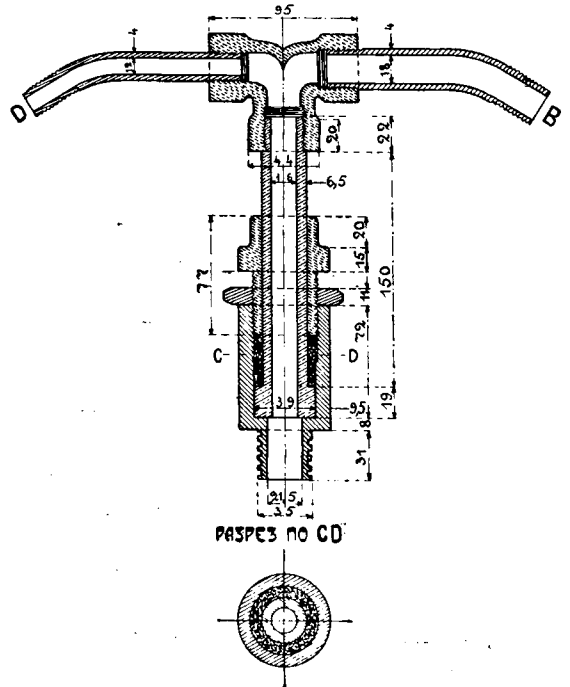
Дробовой распределитель при станках „Крелиус“.
